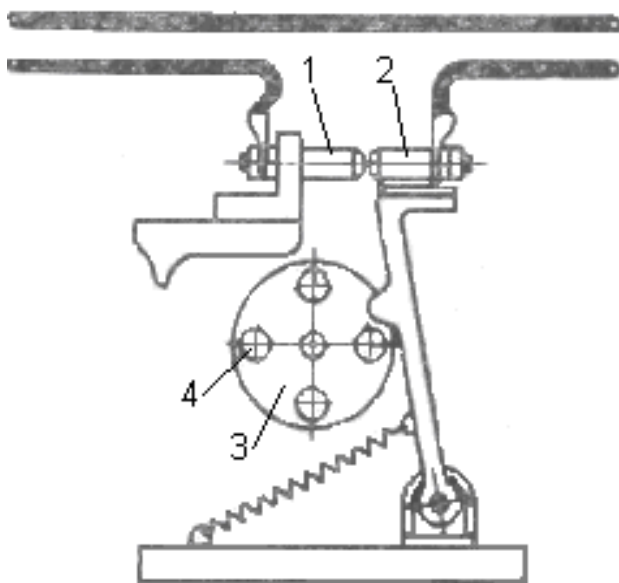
Механический асинхронный прерыватель кулачкового типа
